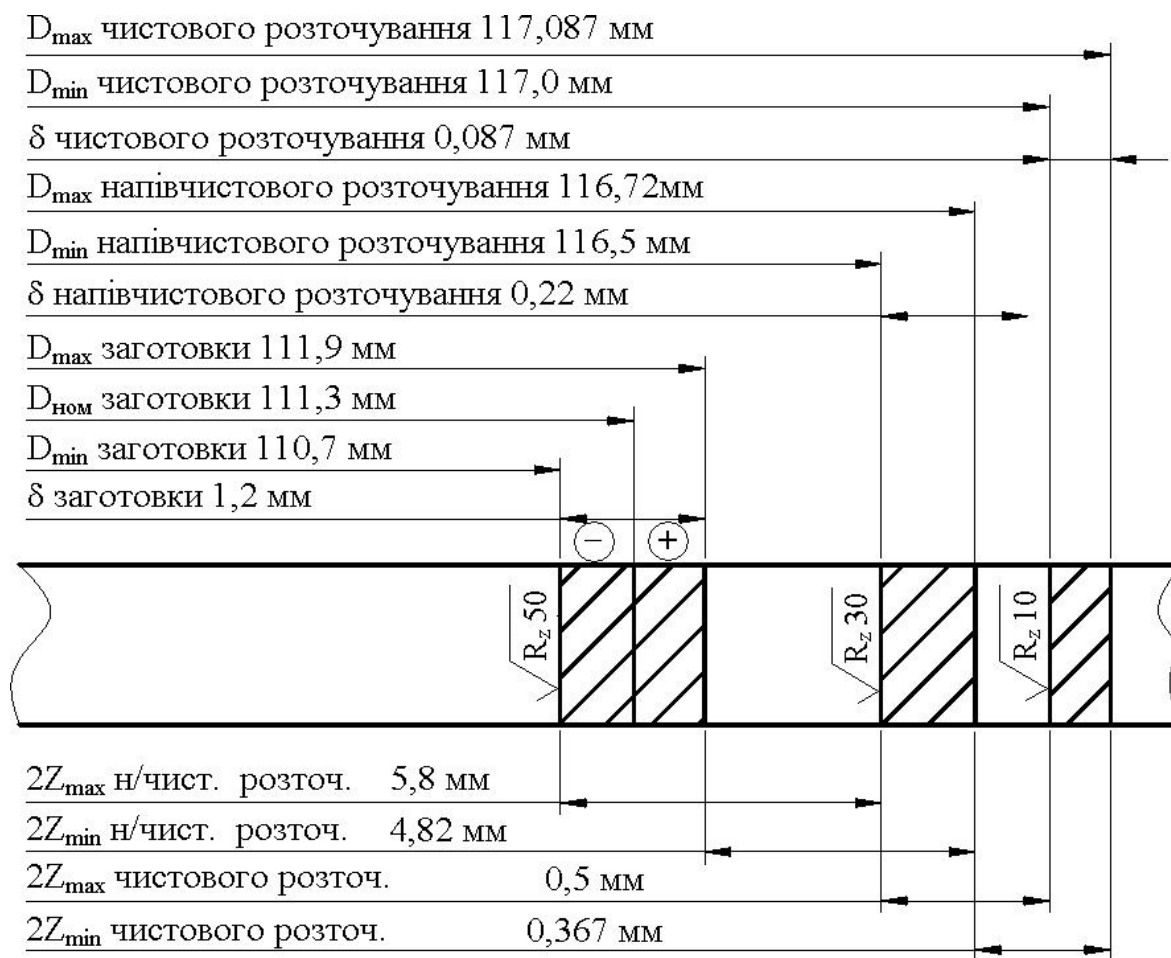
Схема розташування припусків та допусків для поверхні
